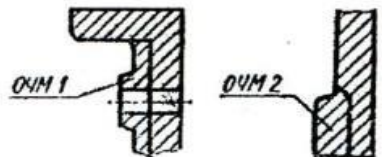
Чертеж отливки с припусками и отверстиями, не выполняемыми в литье
